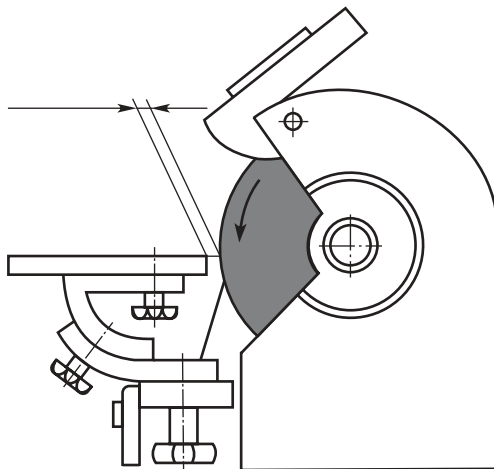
Расположение подручника и шлифовального круга при заточке резца на точильно-шлифовальном станке
